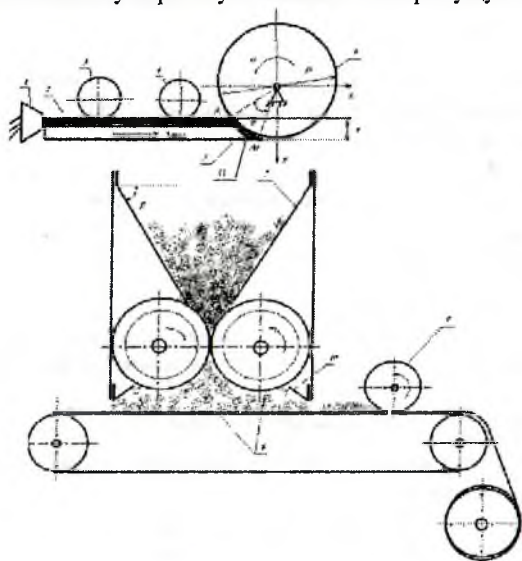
Схема устройства для непрерывного валкового нанесения штапелированных нитей на основу
